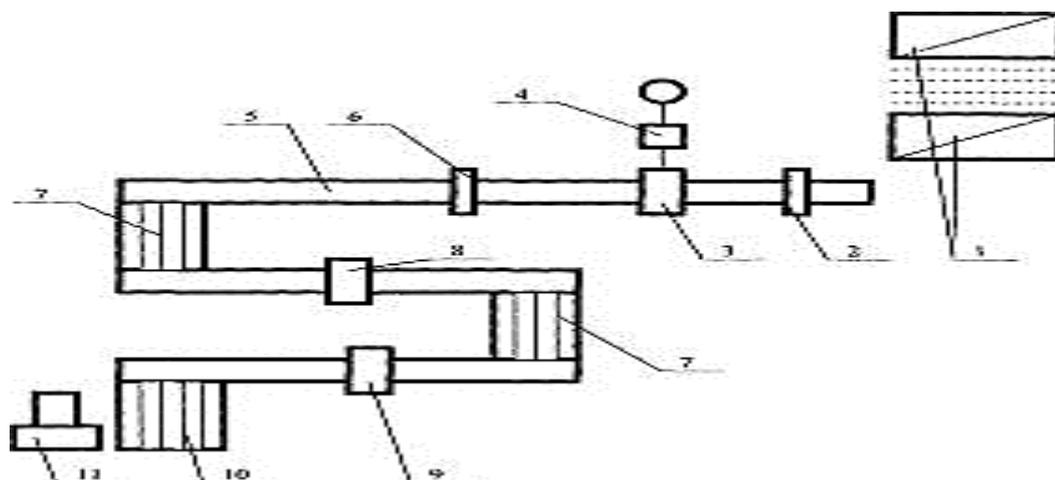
Схема расположения оборудования толстолистого стана «3500»: 1- нагревательные печи; 2- механический окалиноломатель; 3- прокатная клеть; 4- шестеренная клеть; 5- рольганг; 6- ножницы поперечной резки; 7- шлепперы; 8-правильная машина; 9- дисковые ножницы; 10- карманы готовой продукции; 11- ножницы для порезки бракованных листов.
